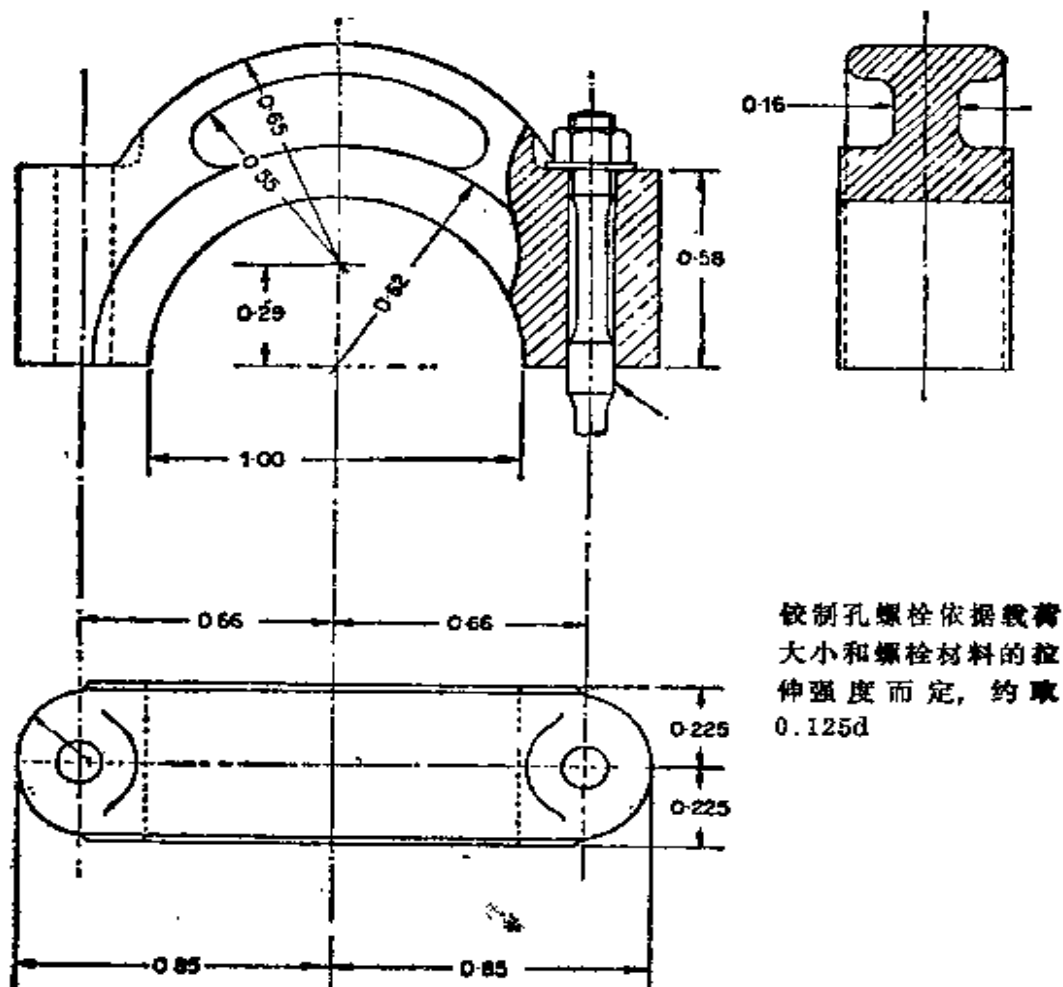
典型的重型轴承轴承盖 (见 9.02 段) 图上各尺寸参数与轴承孔成比例, 因此取它为 1.00
